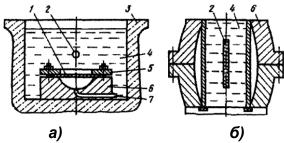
Схема штамповки взрывом деталей из плоской (а) и трубной (б) заготовки в стационарном бассейне:
